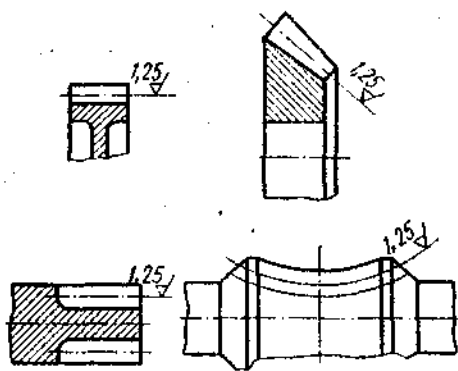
Нанесение обозначения шероховатости поверхностей зубьев и шлицев
